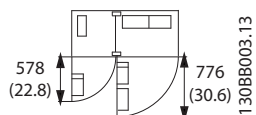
Пространство перед корпусом типа IP21/IP54, типоразмер F9
